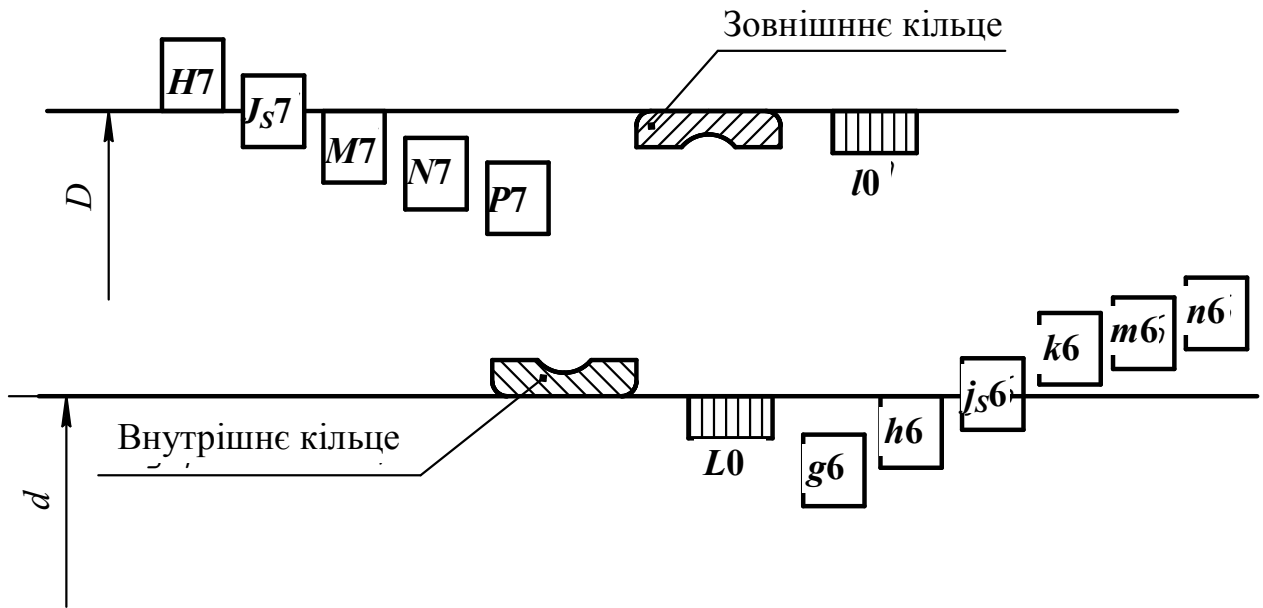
Схема розташування полів допусків при посадках підшипників на вали та в отвори корпусів на прикладі підшипника 0-го класу точності
